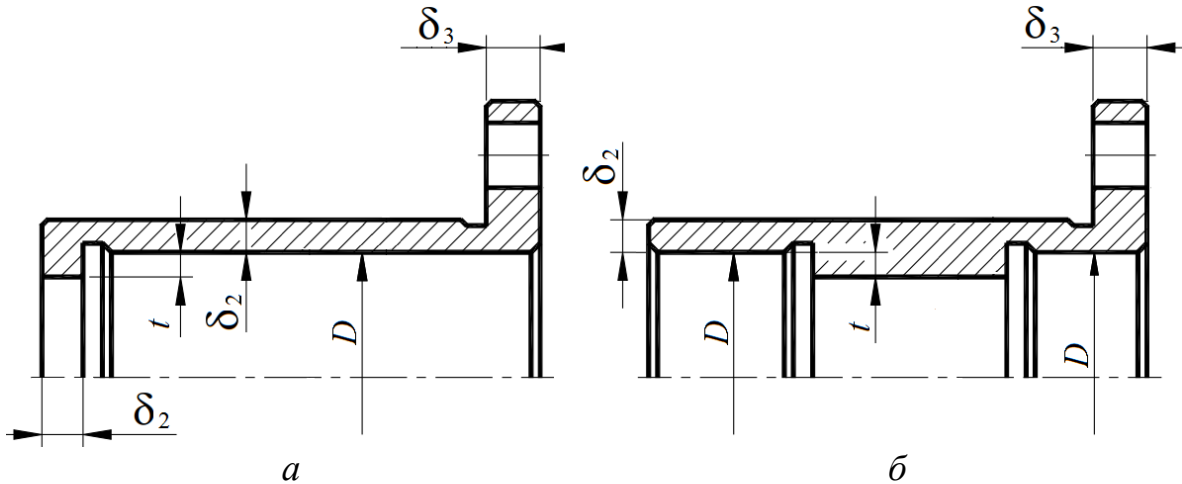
Стакан для підшипників ведучого валу конічної чи черв'ячної передачі:
